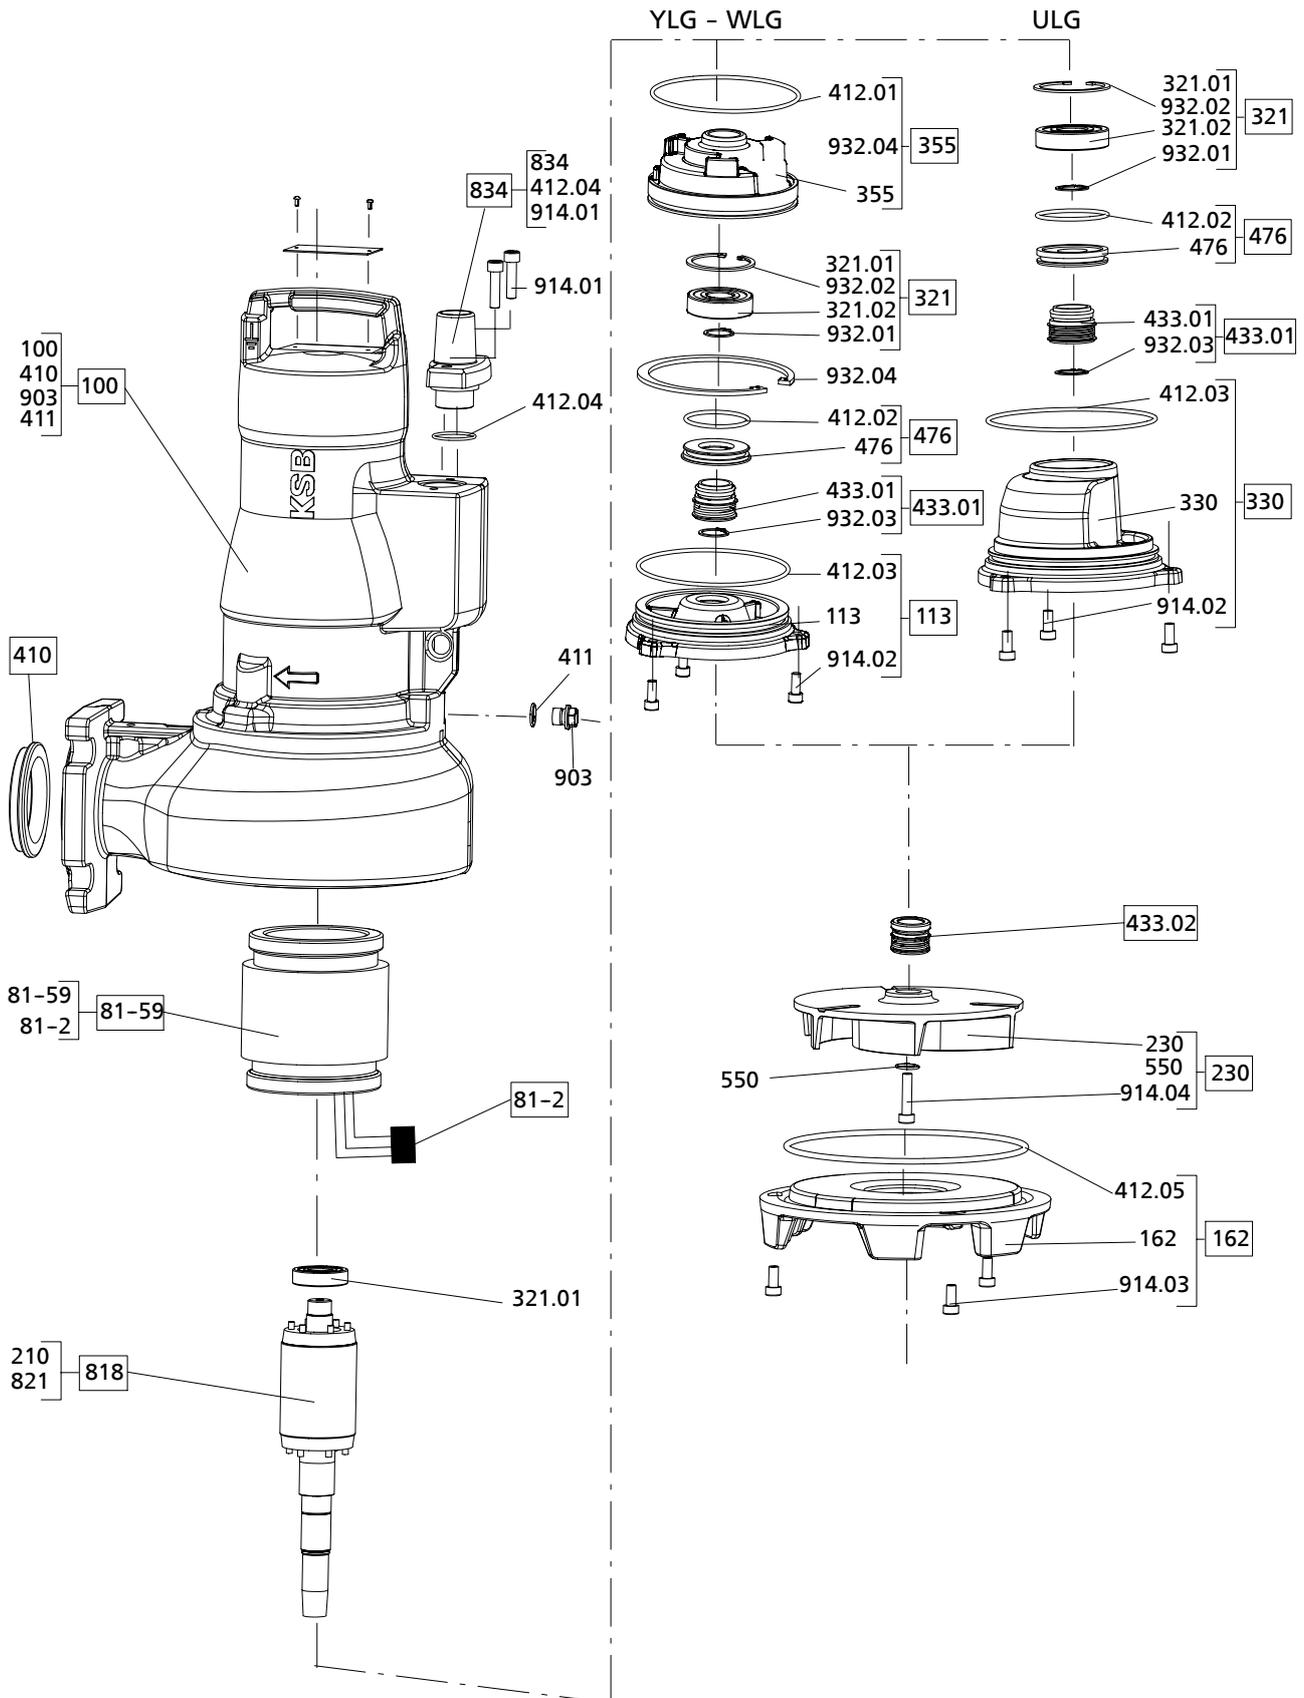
Explosionszeichnung Amarex N mit F 50 - 100
